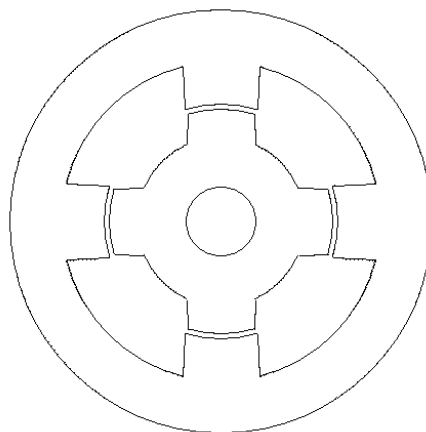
Двухфазный ВРД конструкции 4/4
